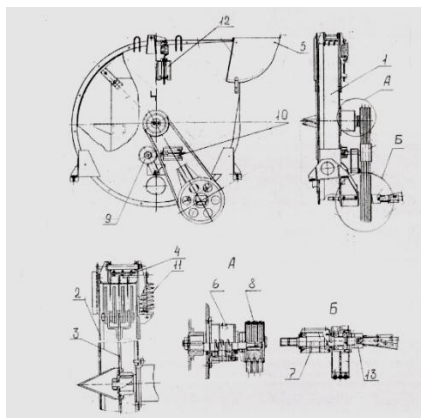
Приспособление для измельчения и разбрасывания подстилки:
